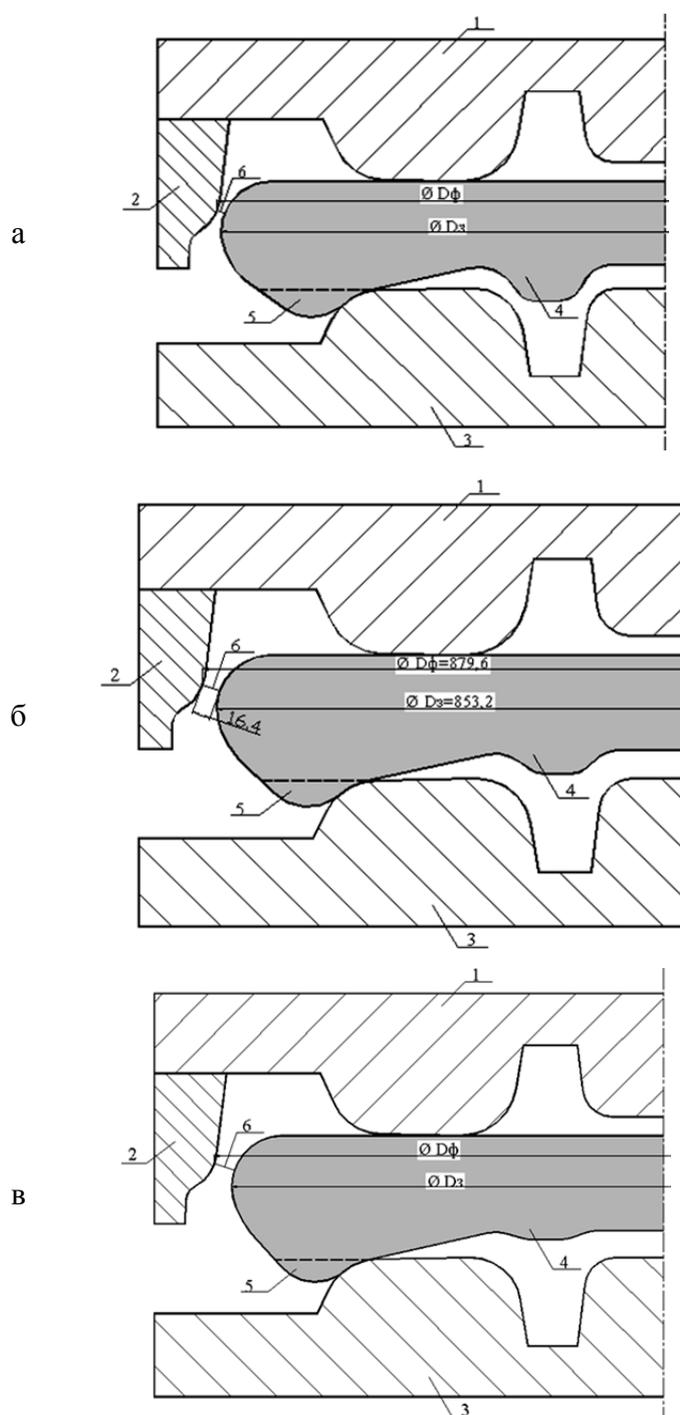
Схема штамповки колесной заготовки, имеющей массу 460 кг, в формовочных штампах:
